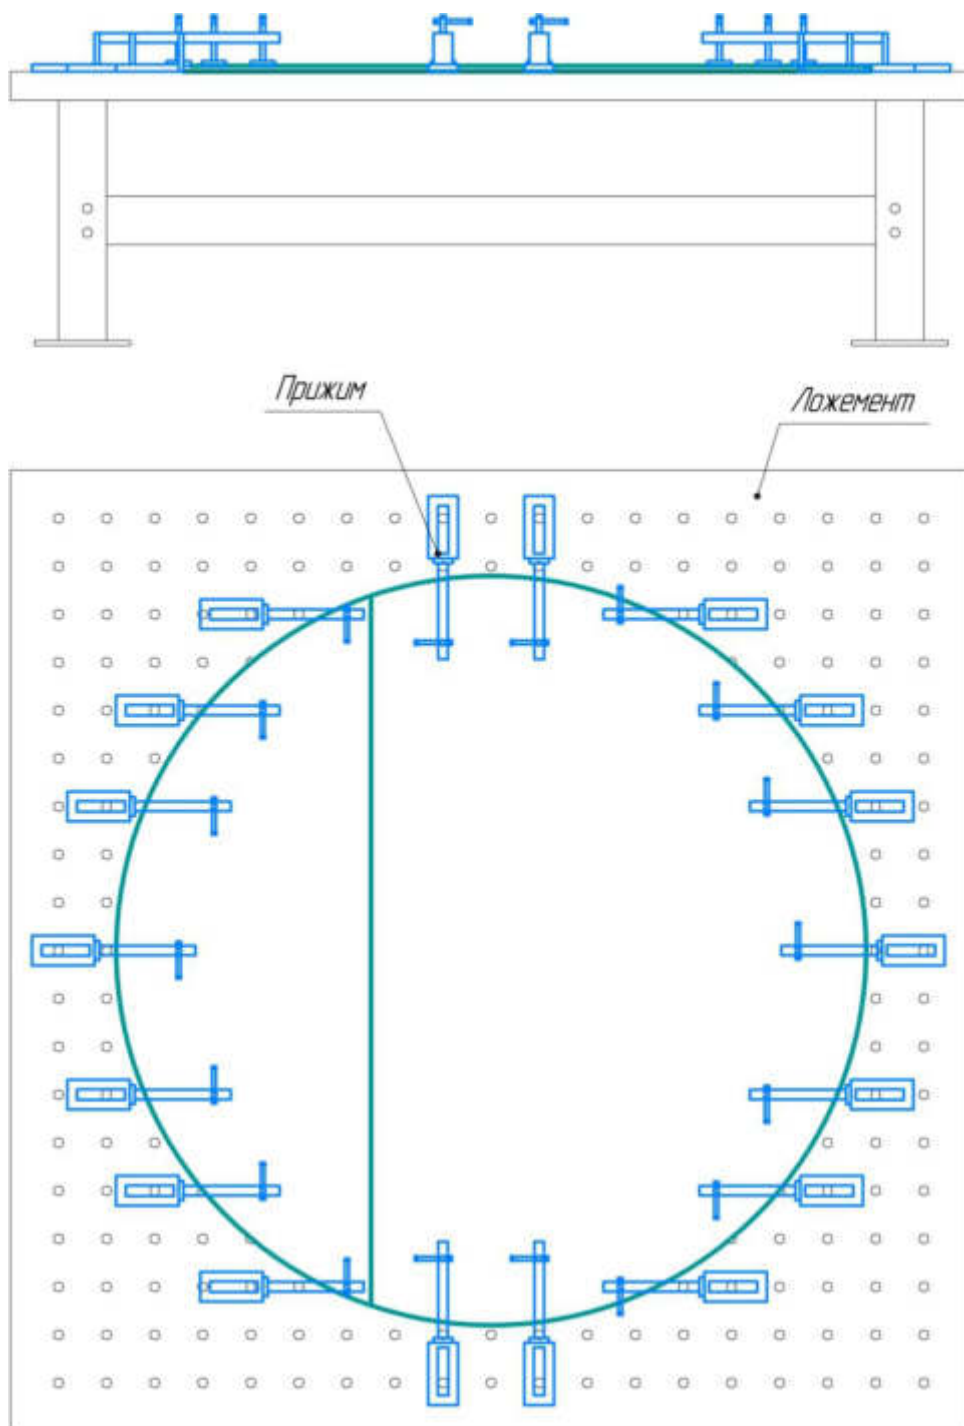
Схема сборки развертки днища верхнего и днища нижнего
